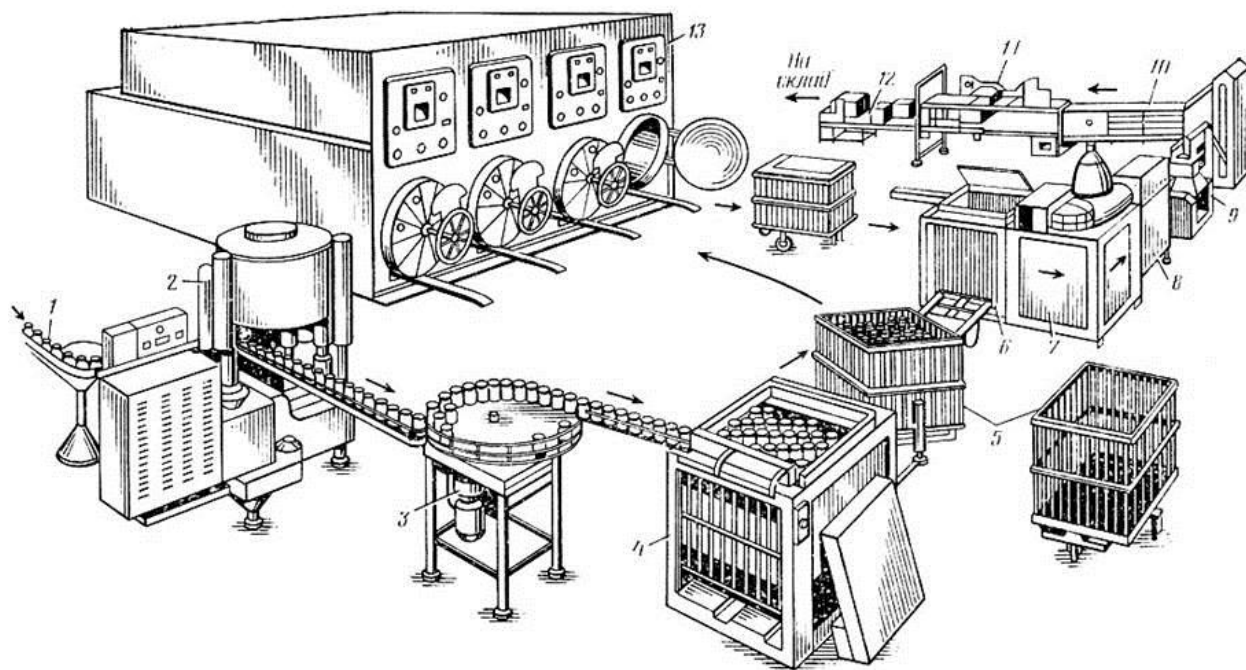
Технологическая линия укупорки, стерилизации и обработки консервов: 1 - транспортер подачи банок; 2 - вакуум-закаточная машина; 3 - стол-накопитель; 4 - устройство для загрузки корзин; 5 - корзины; 6 - устройство для загрузки корзин; 7 - установка для мойки банок; 8 - установка для подсушки банок; 9 - этикетировочная машина; 10 - машина для укладки банок в короба; 11 - машина для оклейки коробов; 12 - транспортер; 13 - стерилизаторы
